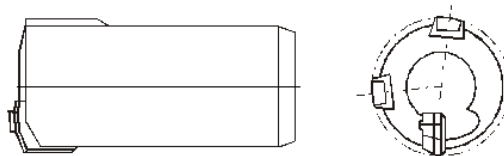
Однолезвийная кольцевая сверлильная головка БТА фирмы «Gebrüder Heller»
